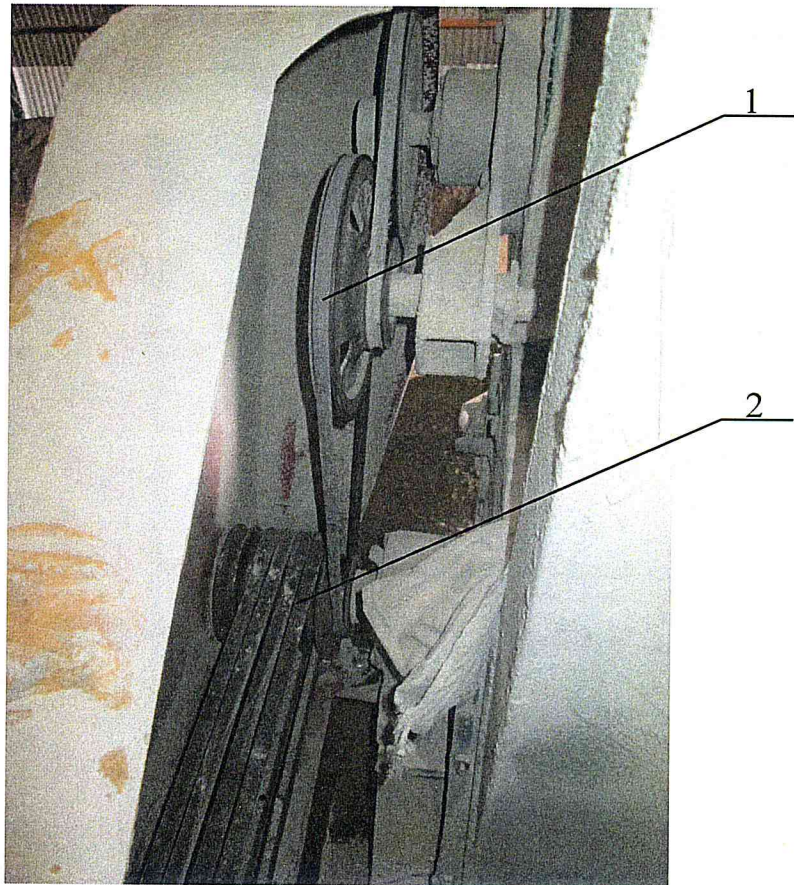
Шкив ременной передачи привода шнека для выгрузки готового продукта (1) и шкив клиноременной передачи привода ротора (2).
